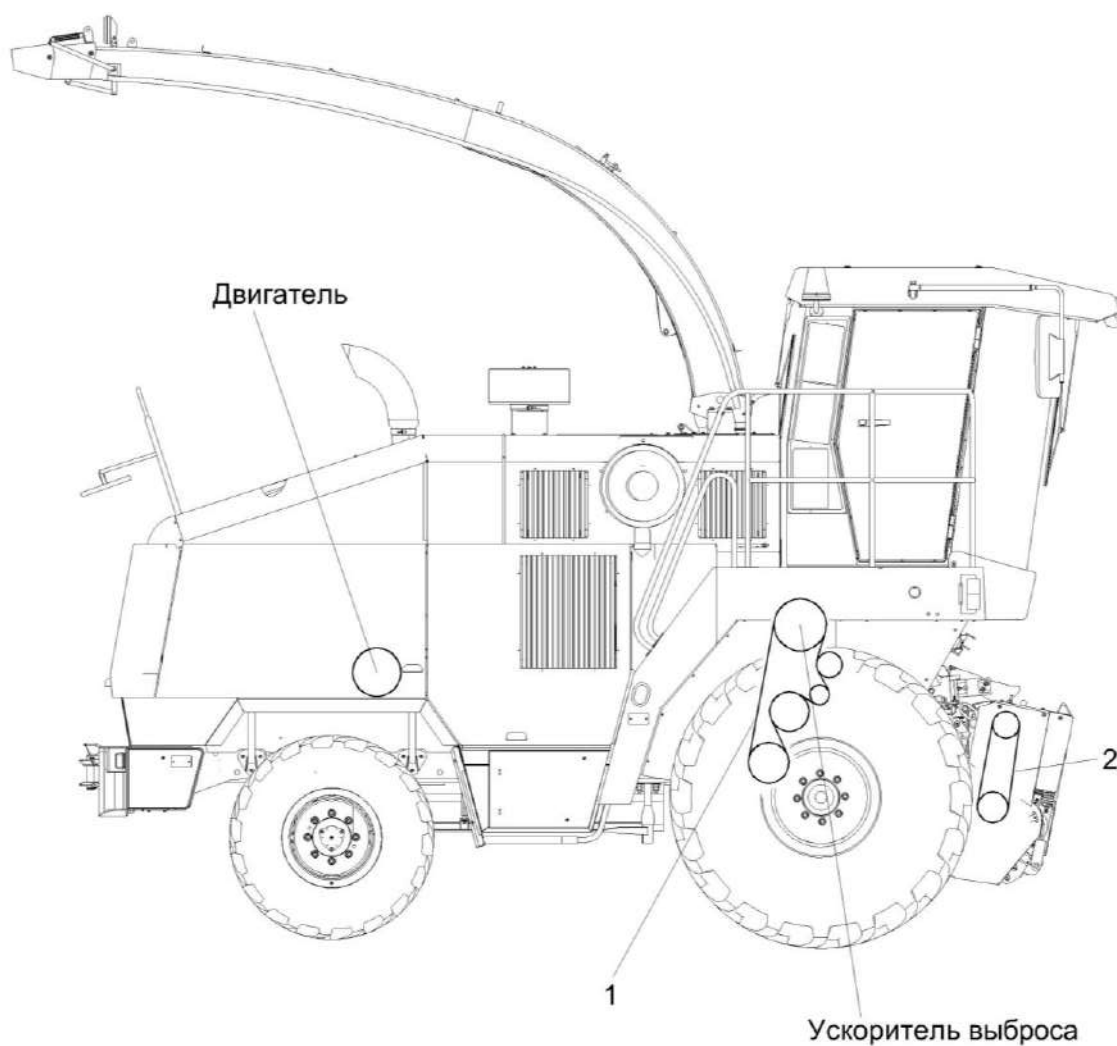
Схема приводов измельчителя (вид справа)
